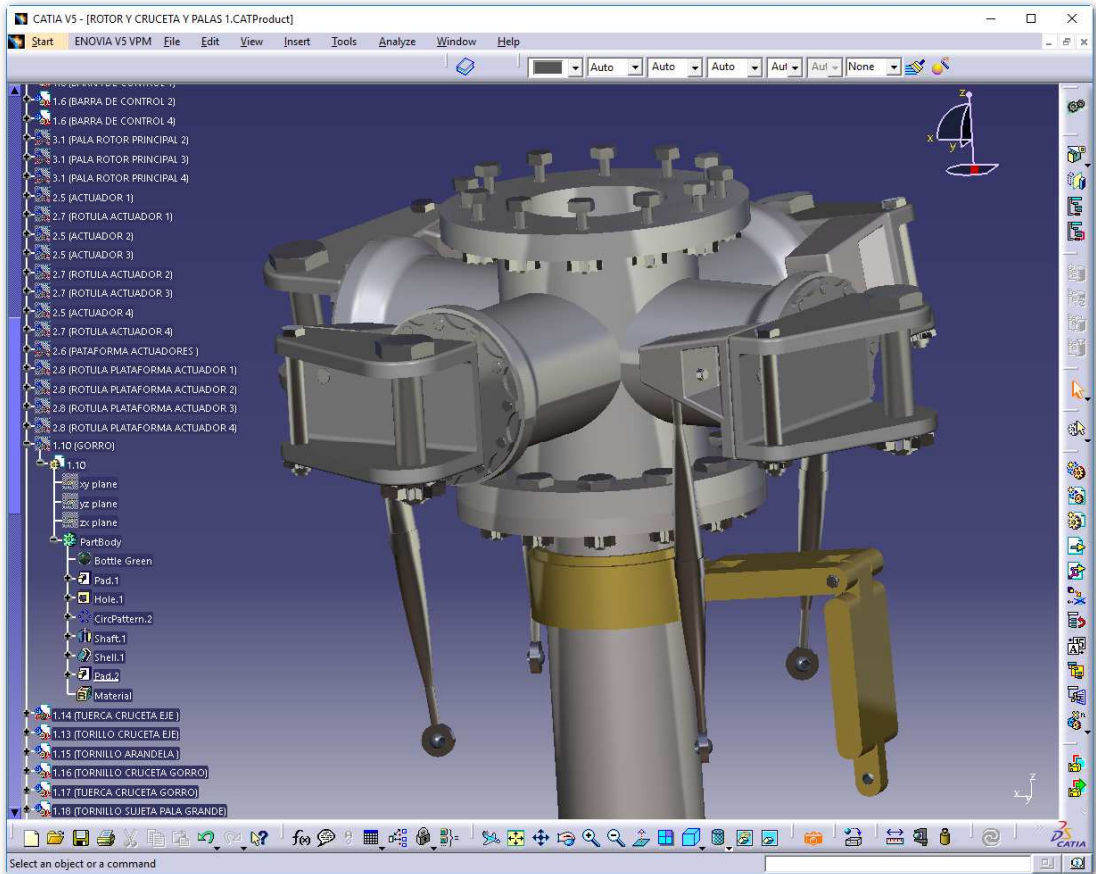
Conjunto cabeza rotor principal sin gorro - material.
